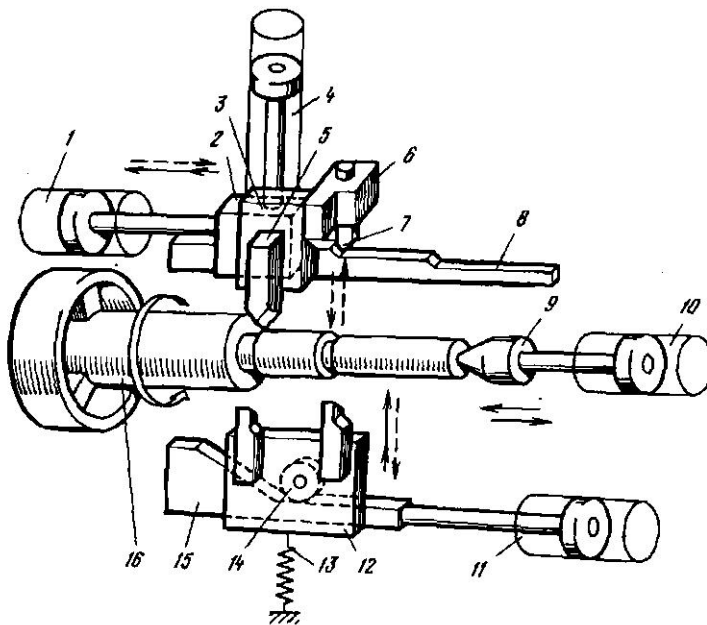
Схема роботи копіювального напівавтомата
